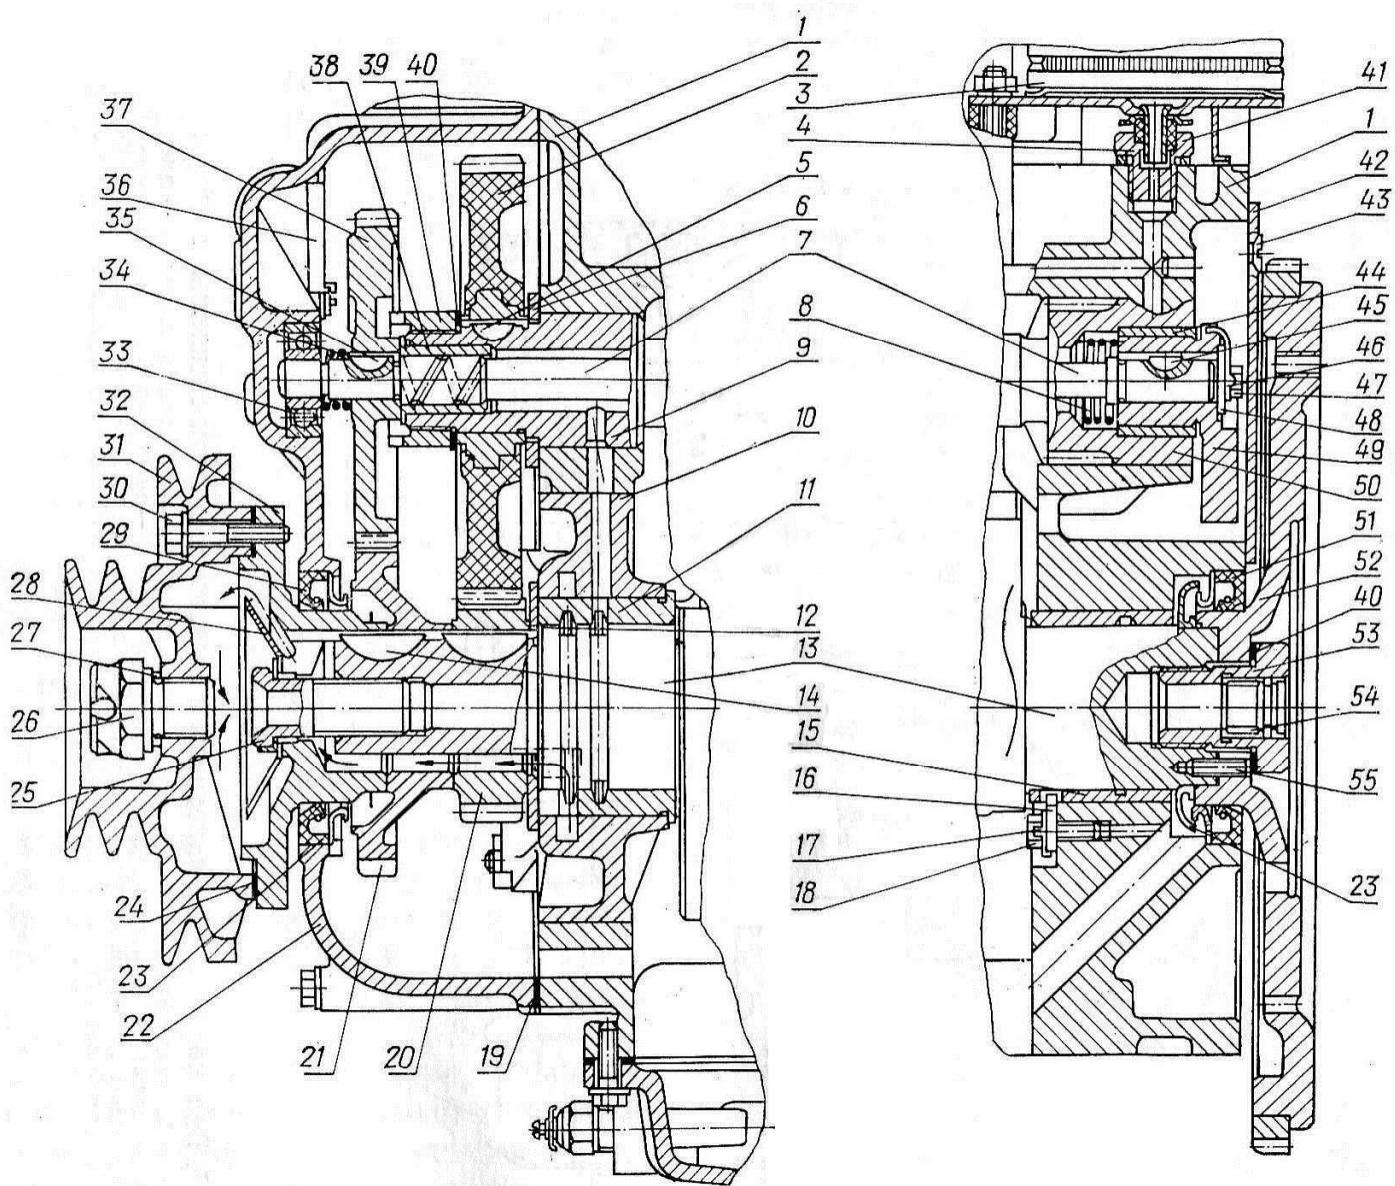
Привод распределительного вала и балансирного механизма, задний коренной подшипник:
